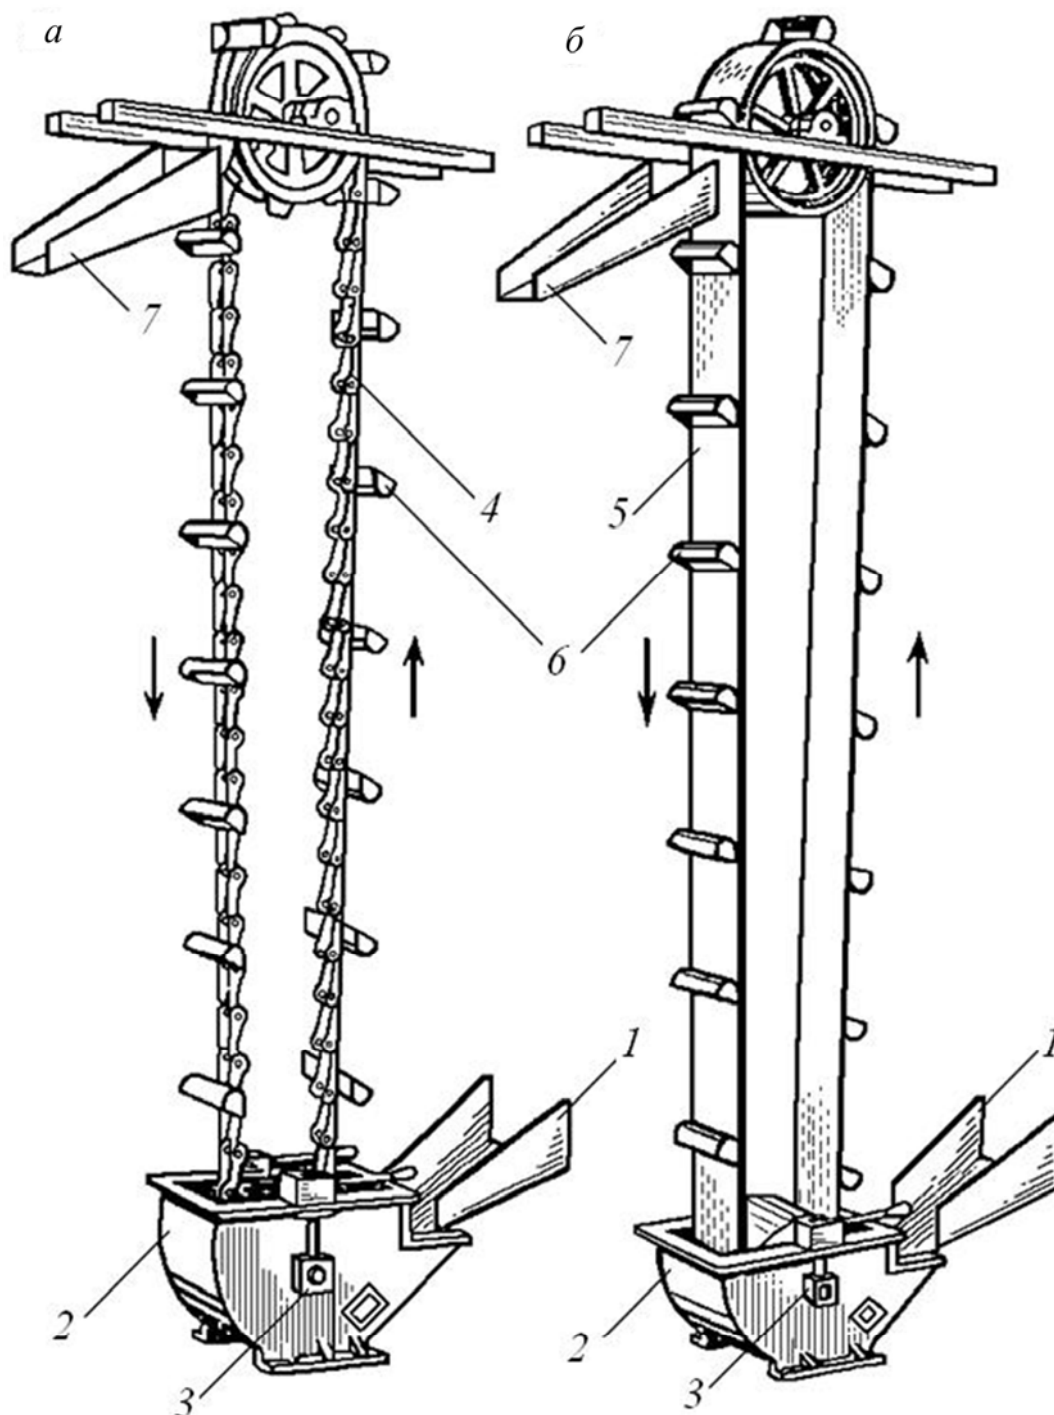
Схемы цепного (а) и ленточного (б) ковшовых элеваторов:
